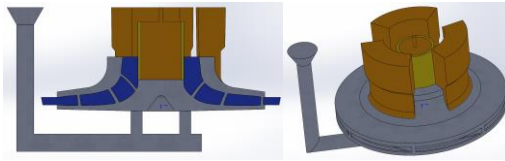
3D модель виливка колеса робочого в зборі
